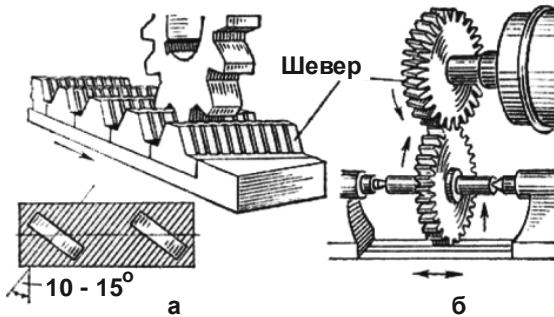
Схема шевінгування циліндричних зубчастих коліс: а – шевером-рейкою; б – дисковим шевером
